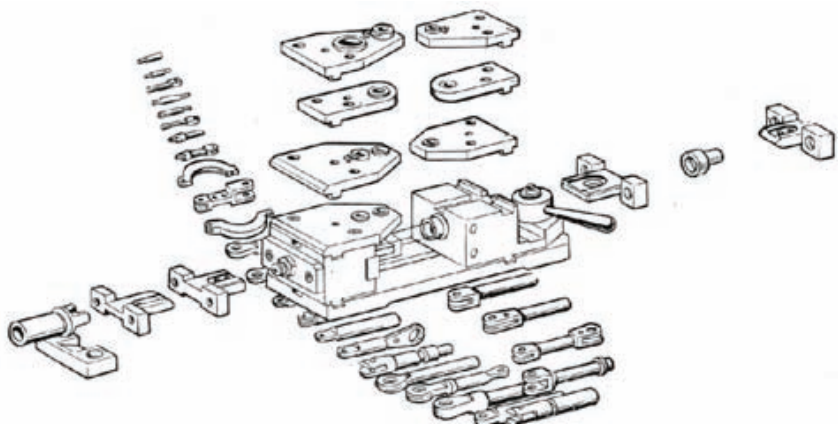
Групповой кондуктор для сверления отверстий в деталях типа валиков и вилок
